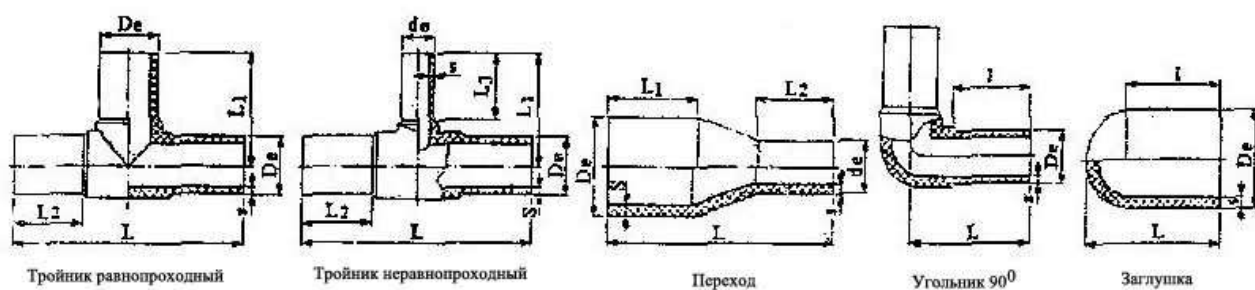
Детали по ТУ 2248-032-00203536-96 для сварки встык или муфтой с ЗН.
